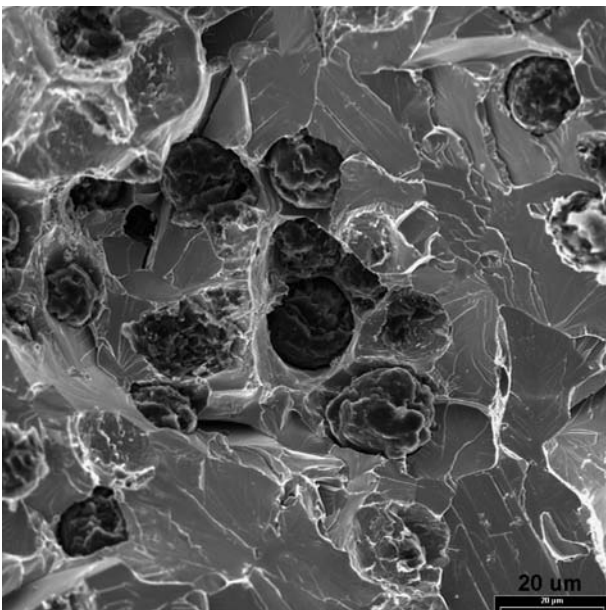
Superficie de fractura de una probeta Charpy del centro térmico del cubo de fundición ensayada a -20 °C:
